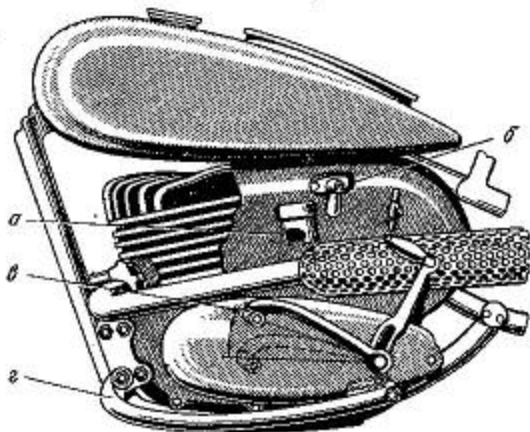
Левая сторона двигателя «ИЖ» с установленным кожухом:
